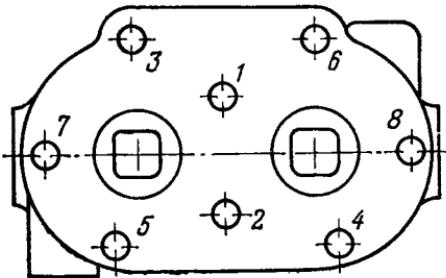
Порядок затяжки гаек шпилек крепления головки цилиндров компрессора
